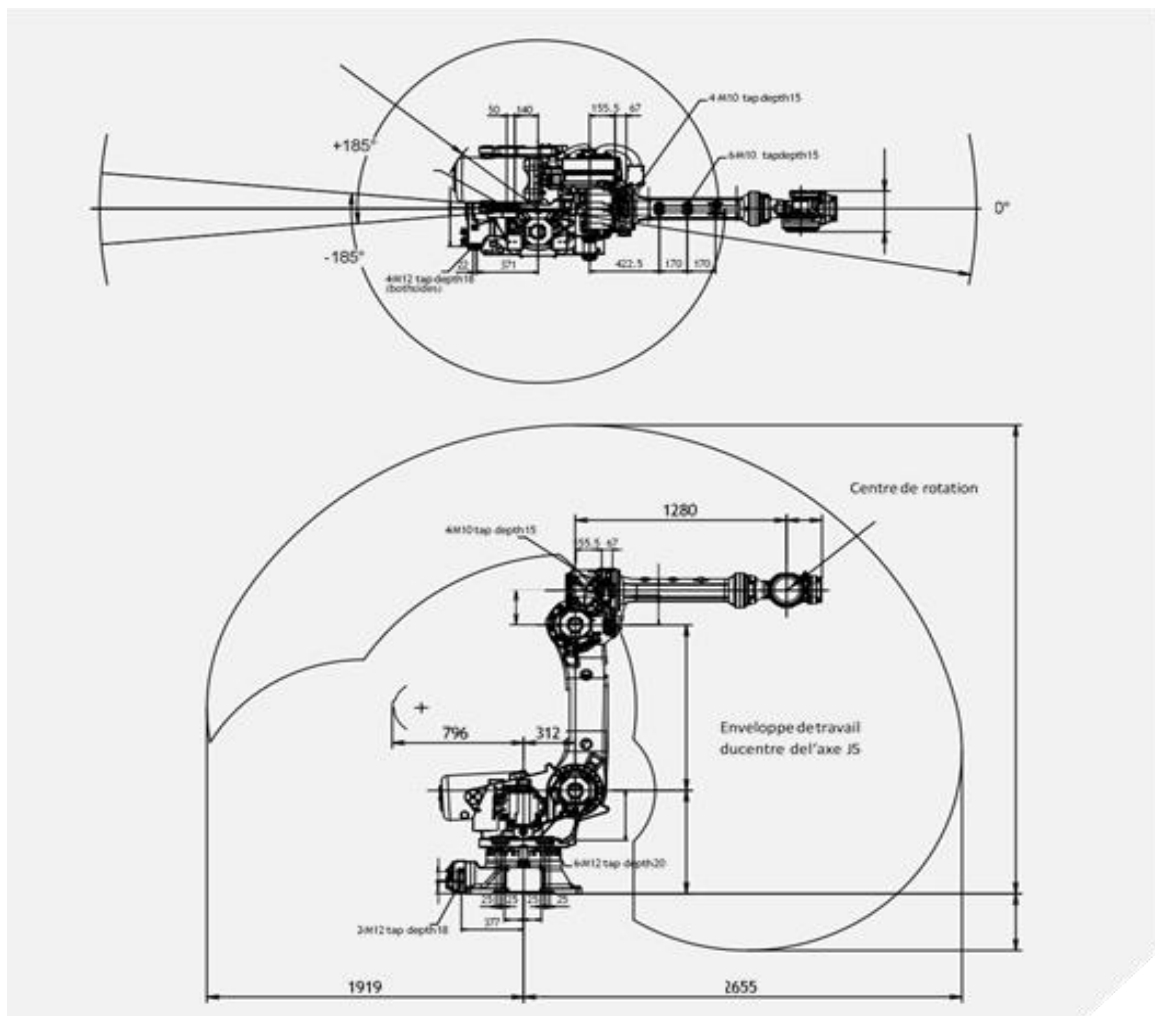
Dimension du robot FANUC R-2000iC/165F.
